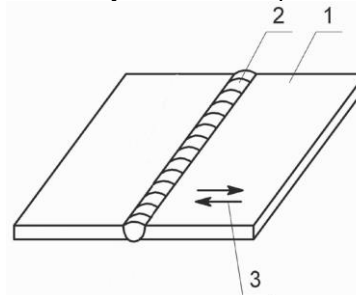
Схема зварювання зразків: 1 – пластины, що зварюються; 2 – зварювальний шов; 3 – напрямок пружних коливань
